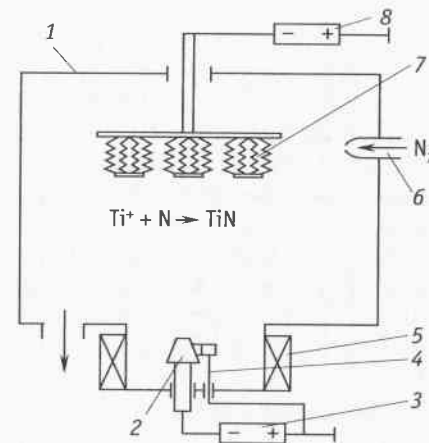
Схема установки для нанесения покрытий на режущий инструмент методом конденсации с ионной бомбардировкой: 1 — корпус вакуумной камеры; 2 — катод; 3 — источник питания разряда; 4 — электрод поджига; 5 — магнитная катушка; 6 — ввод реакционного газа; 7 — режущий инструмент; 8 — источник опорного напряжения
